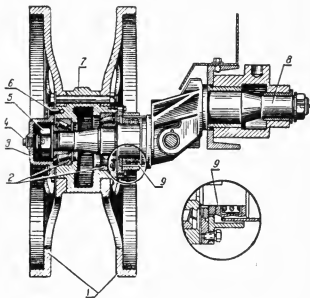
Регулировка подшипников натяжных колес тракторов ДТ-54, ДТ-54А и Т-75:
